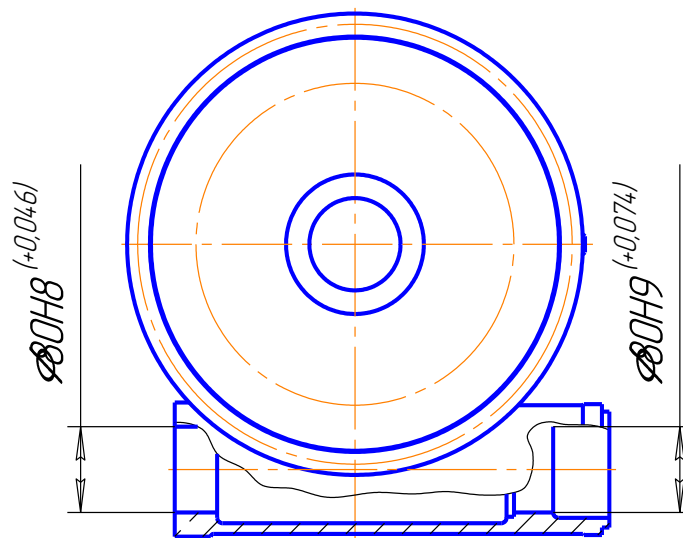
Ескіз обробки поверхні  $\varnothing 80H9^{(+0,074)}$
